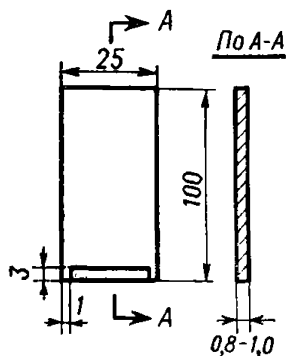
Шпатель из стали марки 08ю или 08кп.
